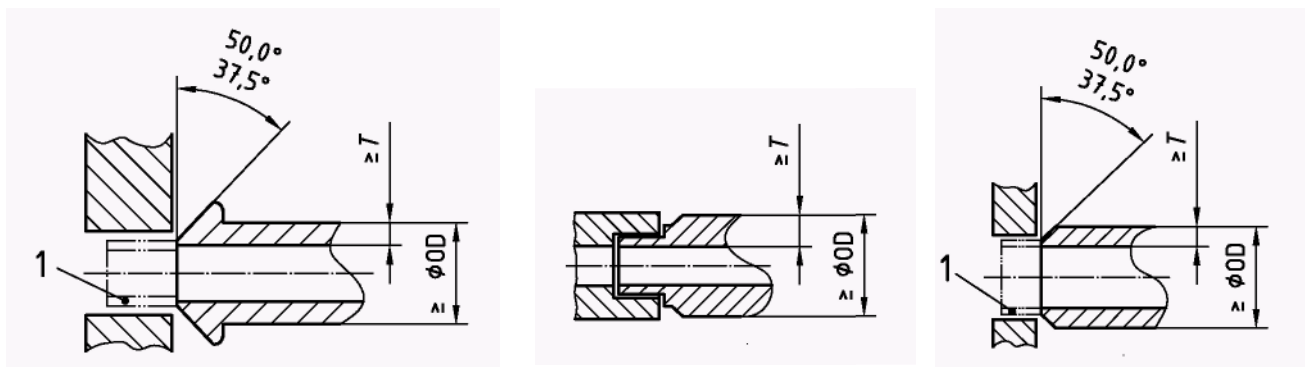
Патрубок с соединением под приварку для Класса 800 и Класса 1500
